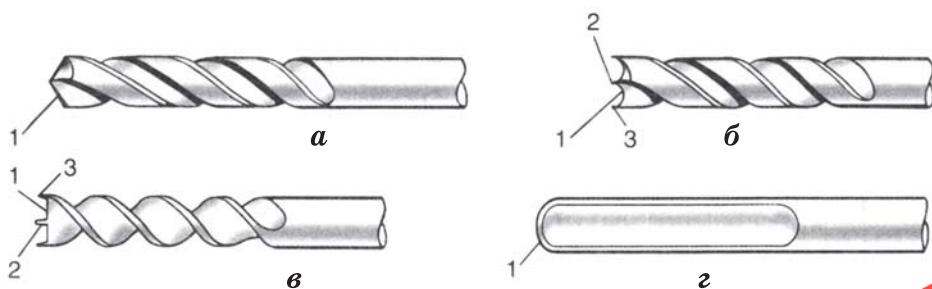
Сверла: а – спиральное; б – центровое, в – шнековое, г – ложечное (1 – режущая кромка; 2 – центр; 3 – подрезатель)
